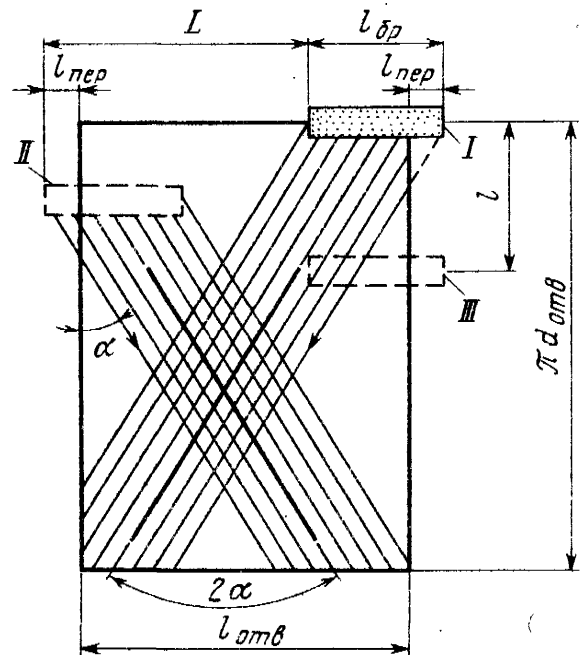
Развертка сетки следов обработки при хонинговании цилиндров блока:
